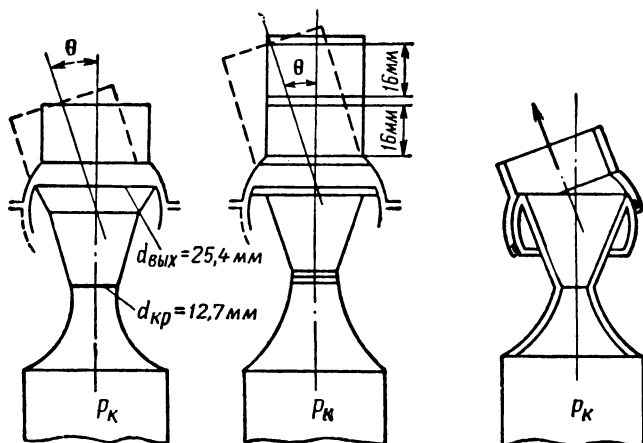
Цилиндрический поворотный насадок для управления вектором тяги
